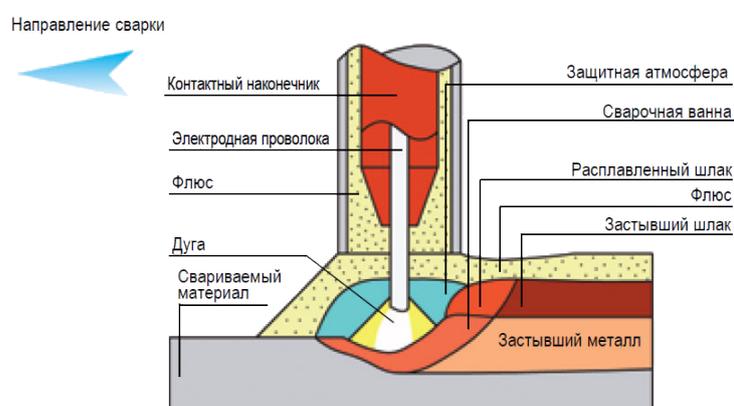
Технология автоматической сварки под флюсом
